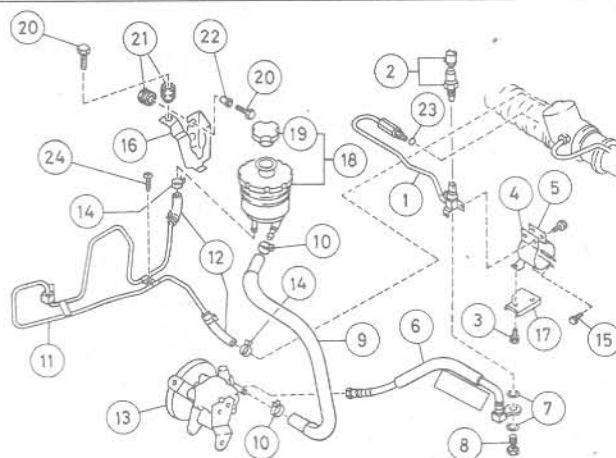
Система труб рулевого управления с гидроусилителем и резервуар (Глава 34)
